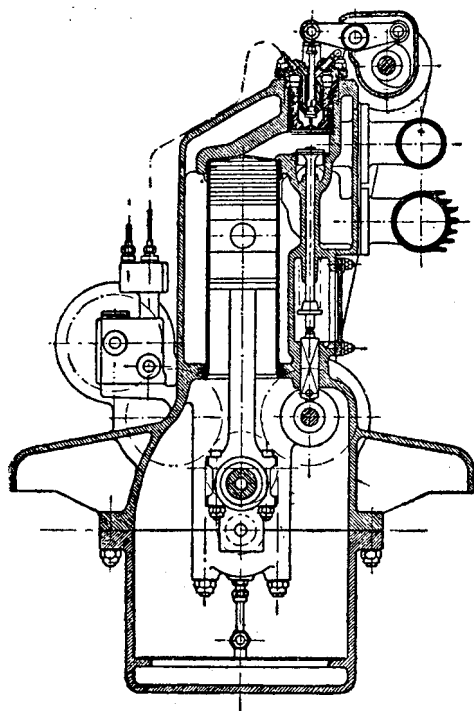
Схема вспрыскивающего устройства компрессорного дизеля Мортон.
